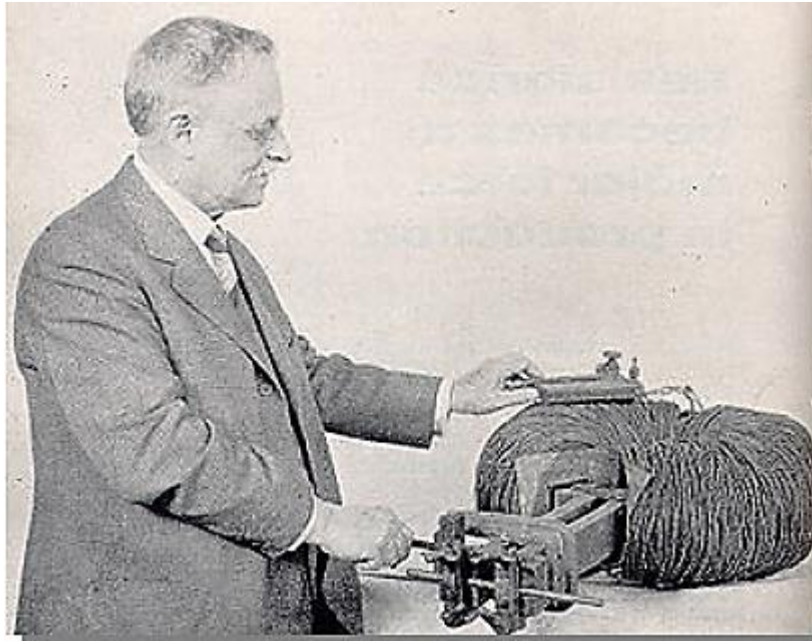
Primera soldadura por resistencia con secundario de bobina simple, construida en 1886, junto a su fabricante Elihu Thompson.
